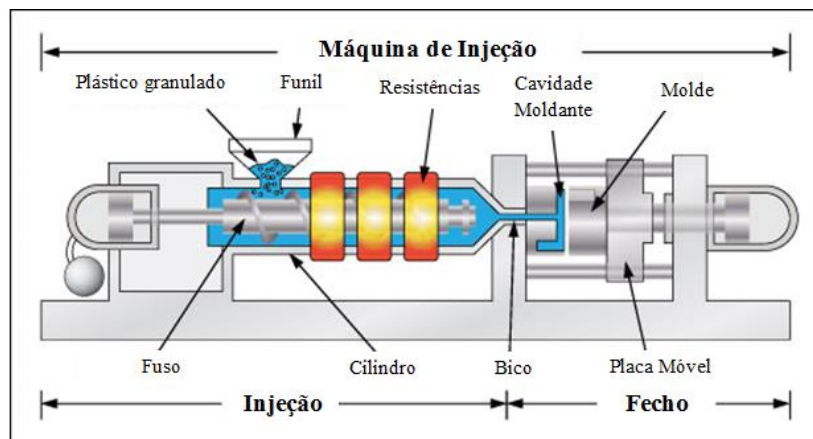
Máquina de moldação por injeção esquematizada, adaptado de (Injection molding machine, 28/Julho/2010)
